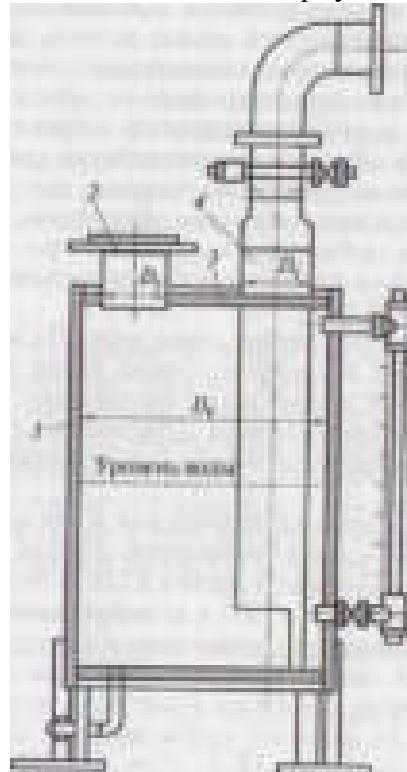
Гидравлический предохранитель: / - корпус; 2 - выходной патрубок; 3 - крышка; 4 - входной патрубок
